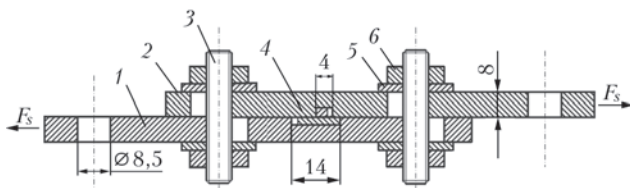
Схема приспособления для испытаний образцов на срез: 1, 2 — соответственно нижняя и верхняя направляющая; 3 — шпилька; 4 — сварной образец; 5 — шайба; 6 — гайка
